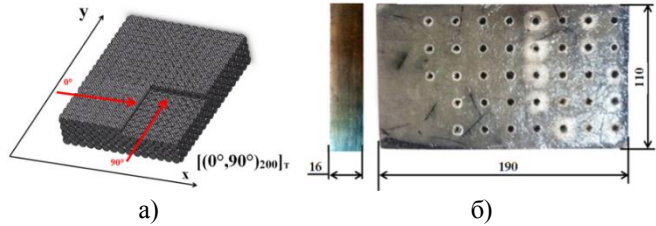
Склопластикова пластина: а – схема армування пластины; б – фото пластины
